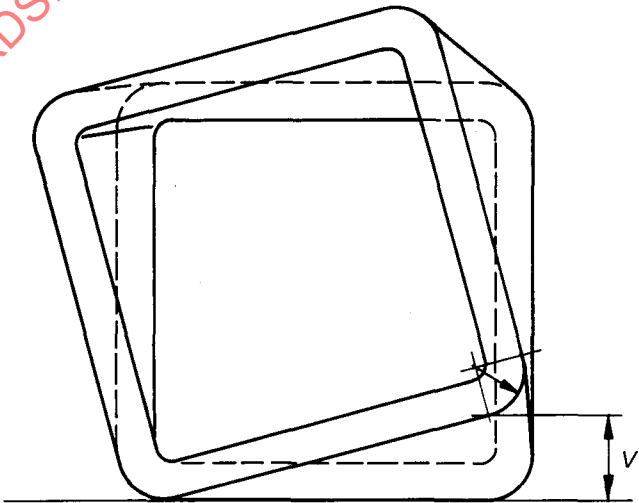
Mesurage du vrillage des sections carrée et rectangulaire
